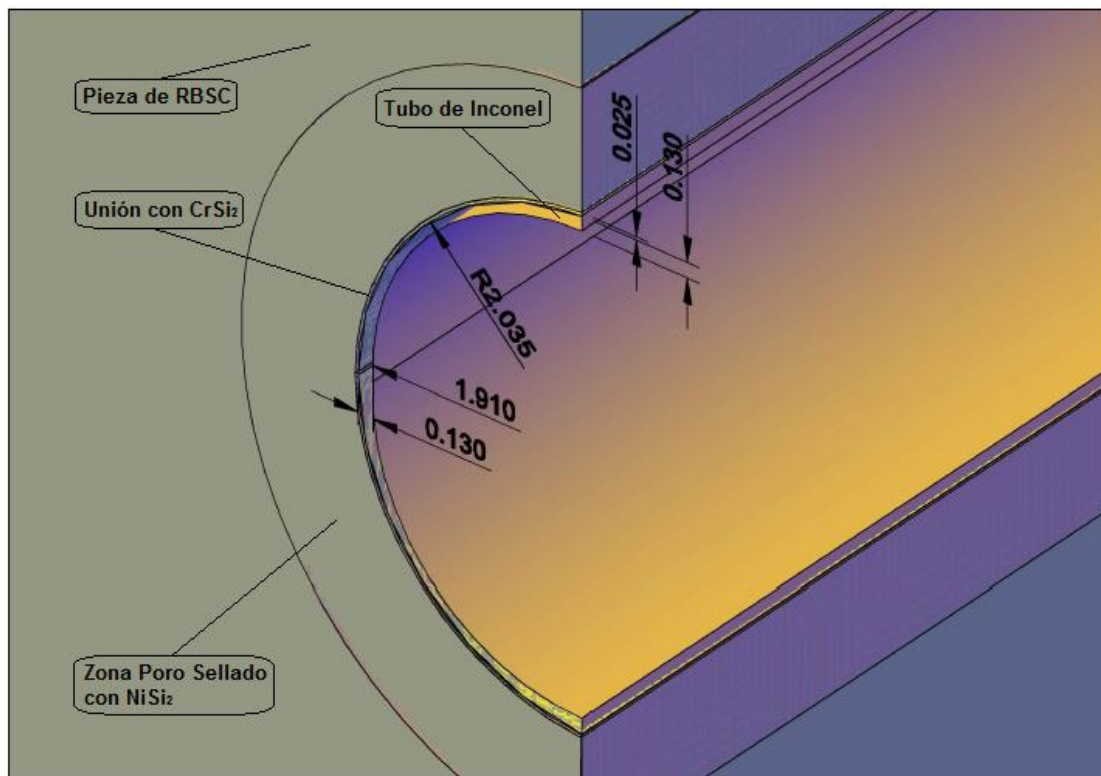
Sección de Pieza con detalle de la unión Tubo-RBSC. Dimensiones en mm.
